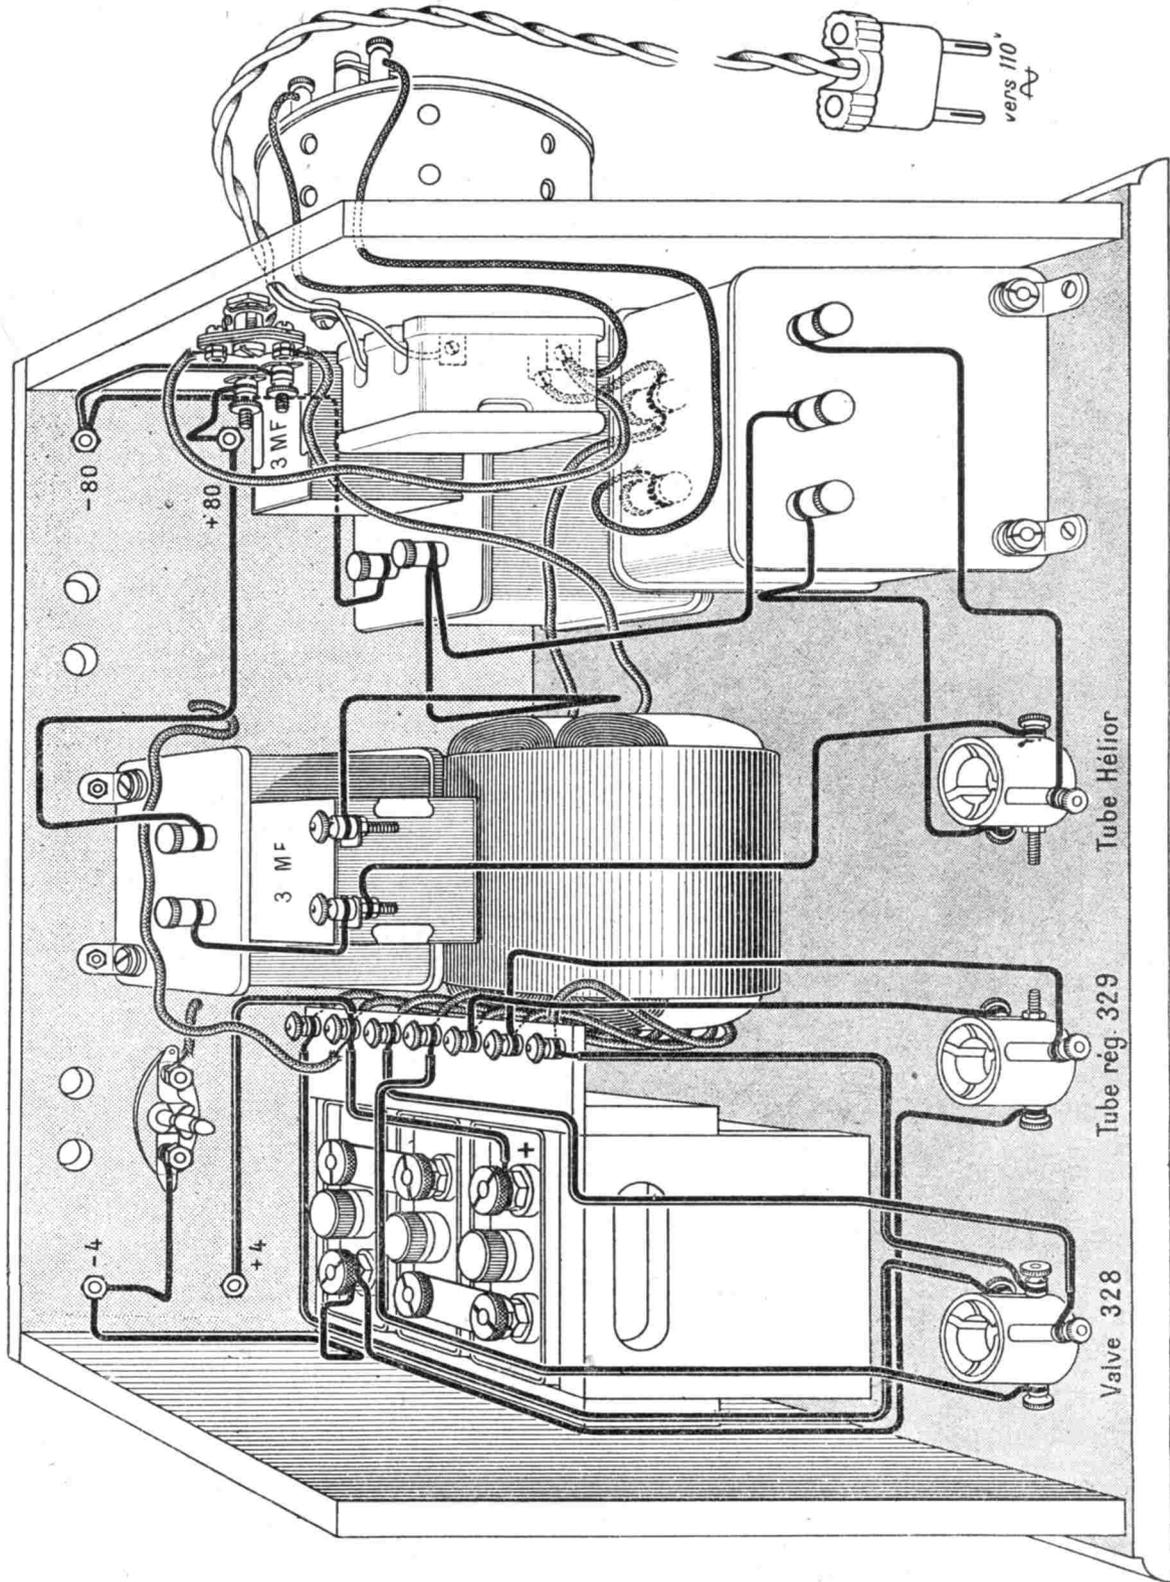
Plan des connexions de la boîte d'alimentation.
